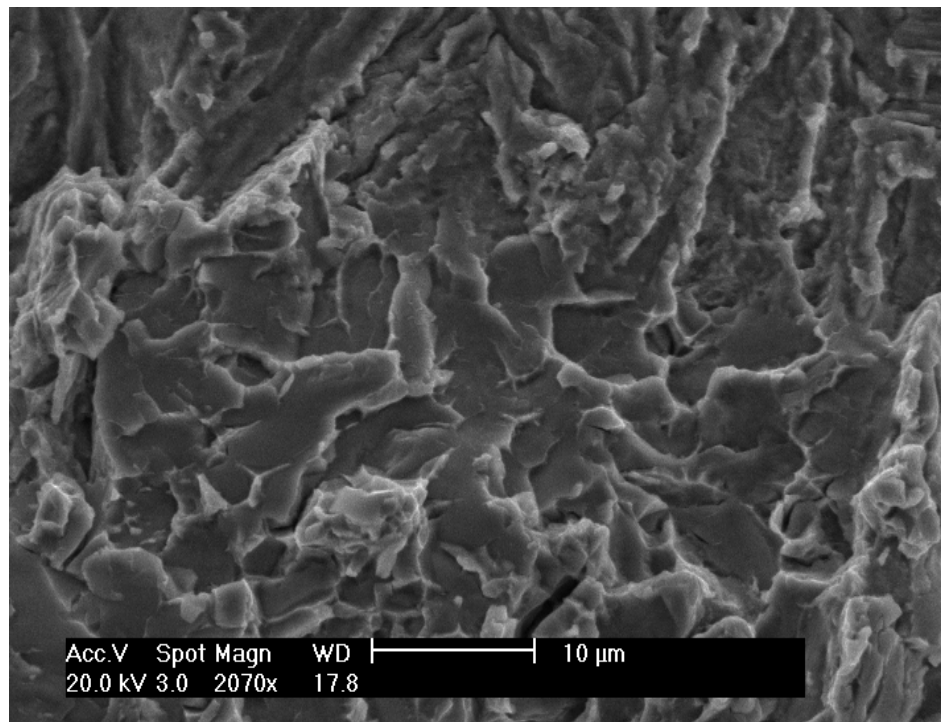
Superfície de fratura do corpo de prova metal de solda 2 fraturado no ensaio de tenacidade a fratura em meio agressivo.
